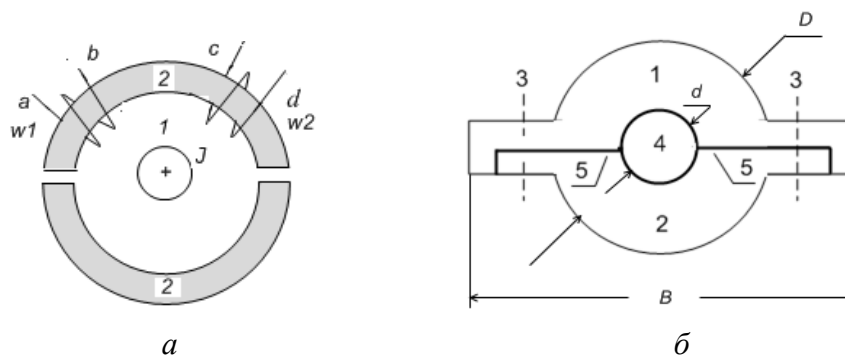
Датчик тока: а – преобразователь величины тока в напряжение; б – вид датчика тока с торца
